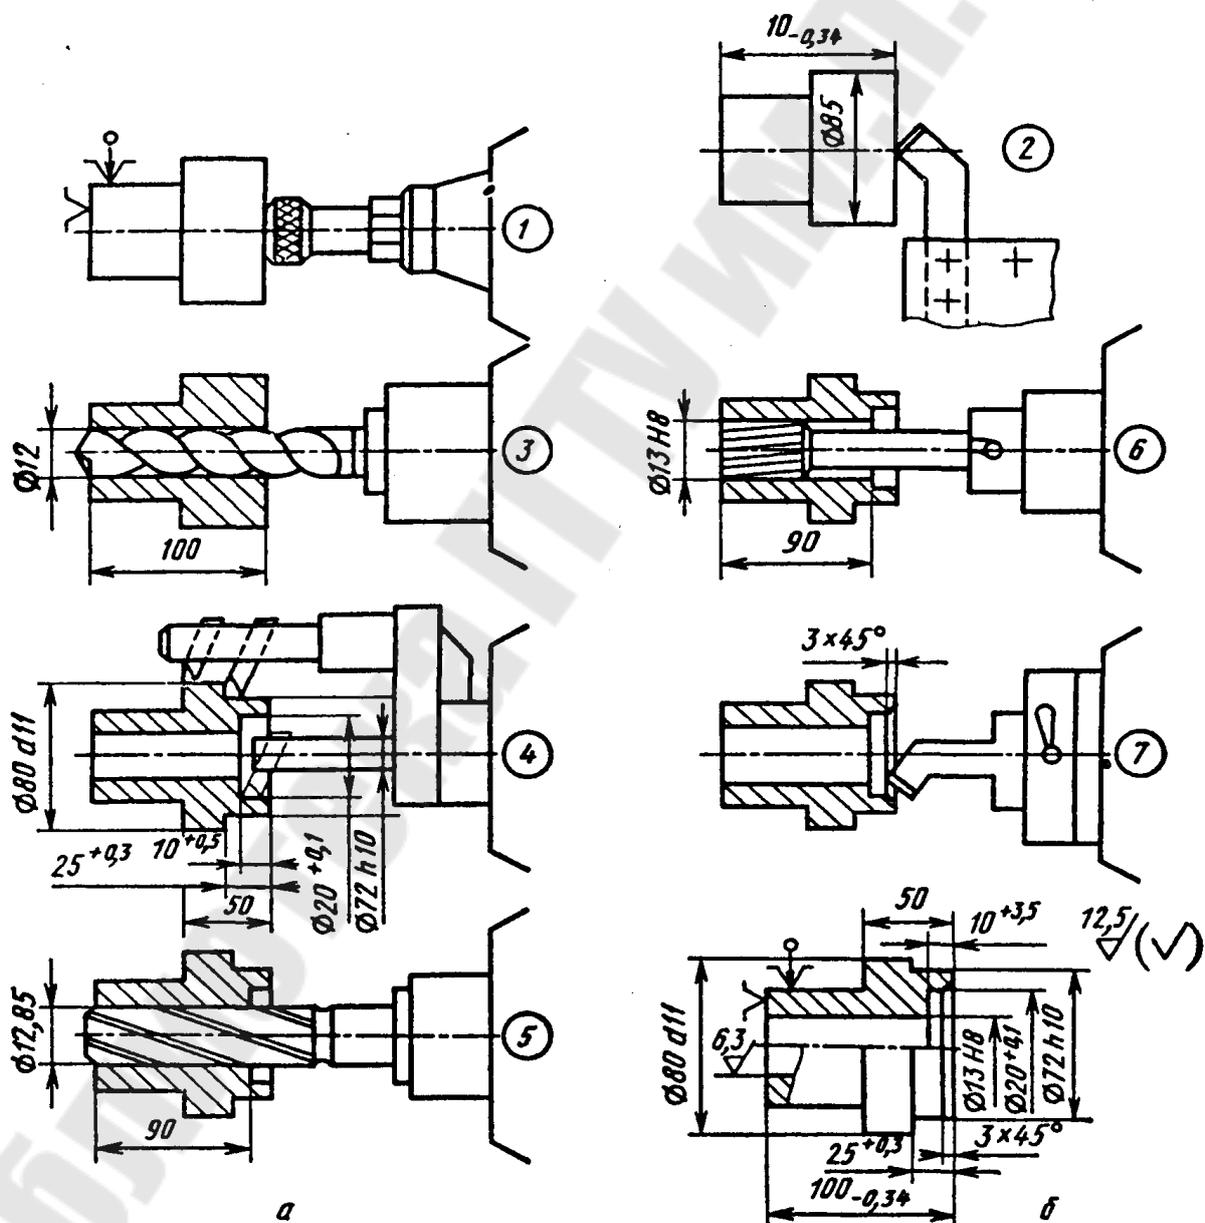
Пример наладки токарно-револьверного станка на обработку типовой детали
